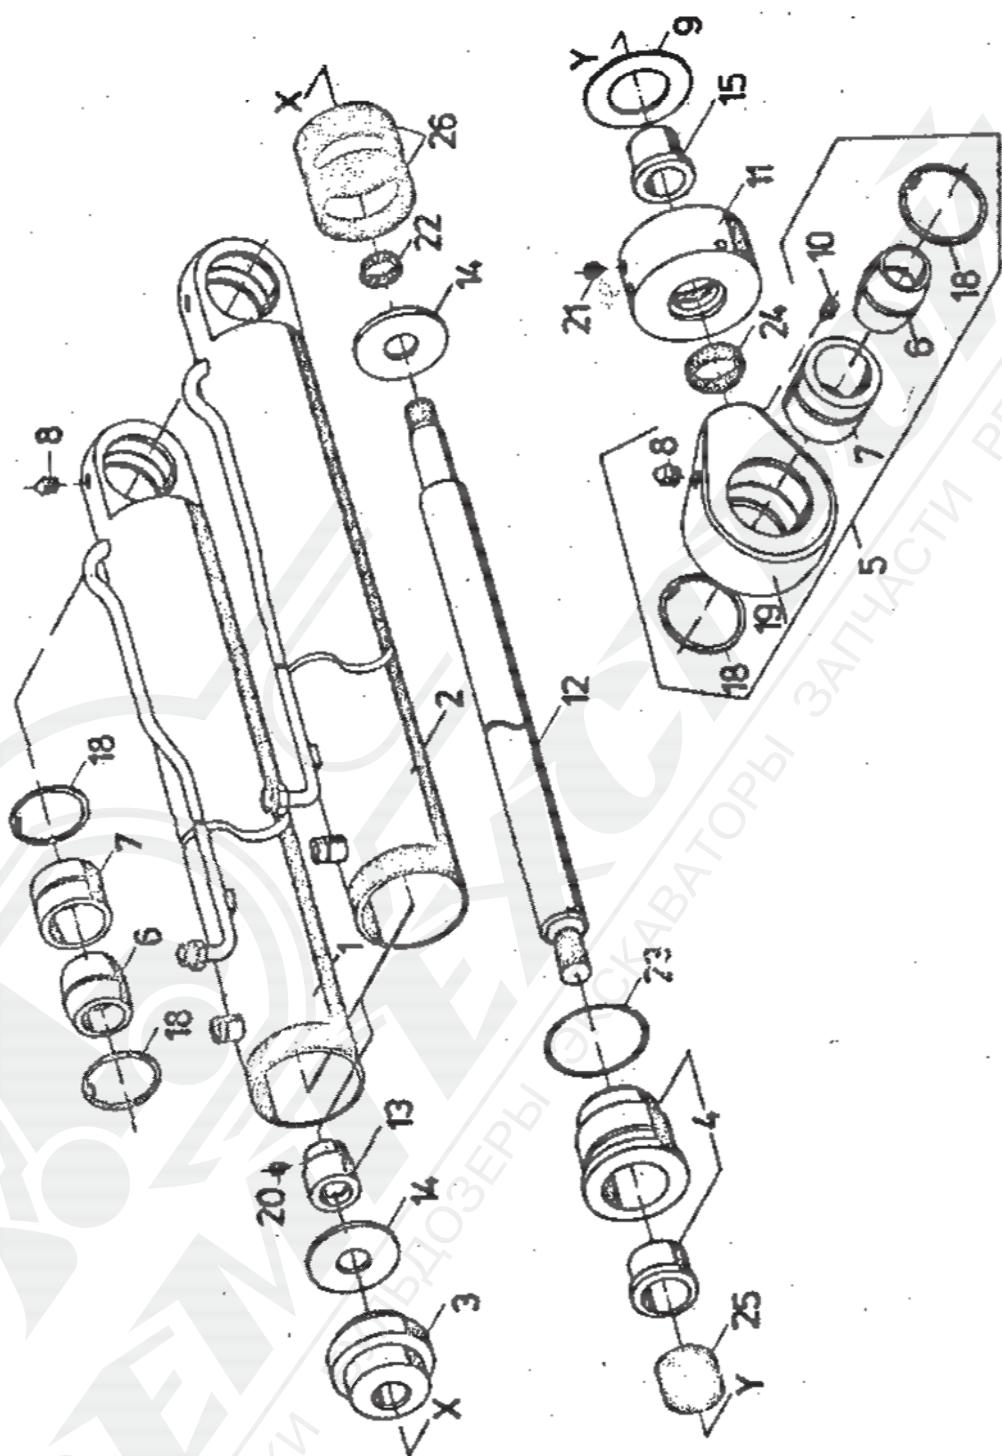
Гидравлический цилиндр подъёма стрелы
